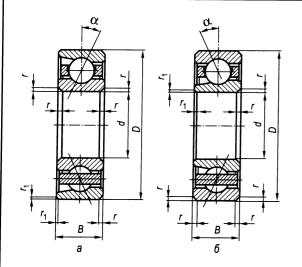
Подшипники шариковые радиально-упорные однорядные размерных серий 36000, 46000 и 66000 (a) и 36000К, 46000К (б)
